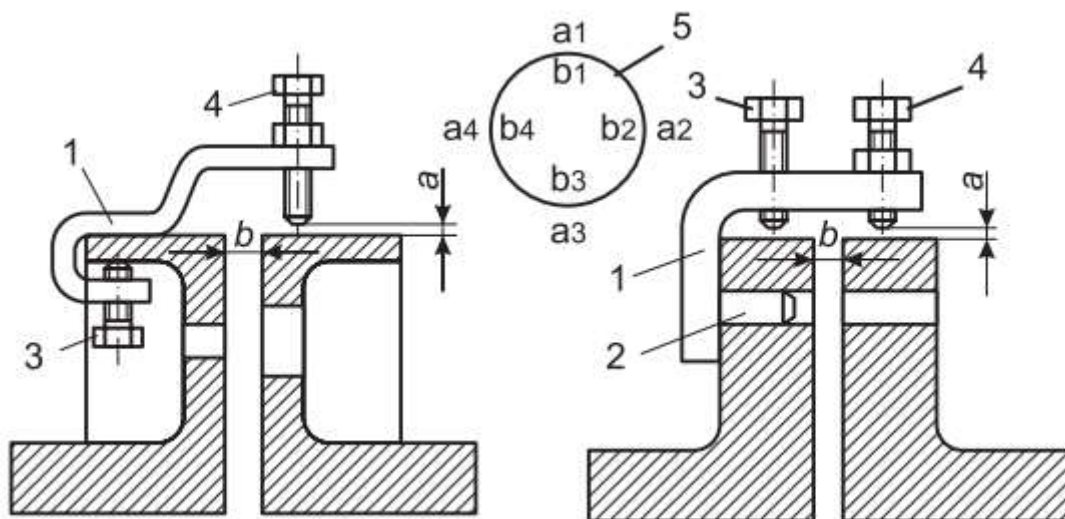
Скобы для центровки электродвигателя с механизмом: *1* — скоба; *2* — палец; *3* — прижимной или стопорный болт; *4* — болт для замера зазора; *5* — рекомендуемая форма записи значений зазоров
